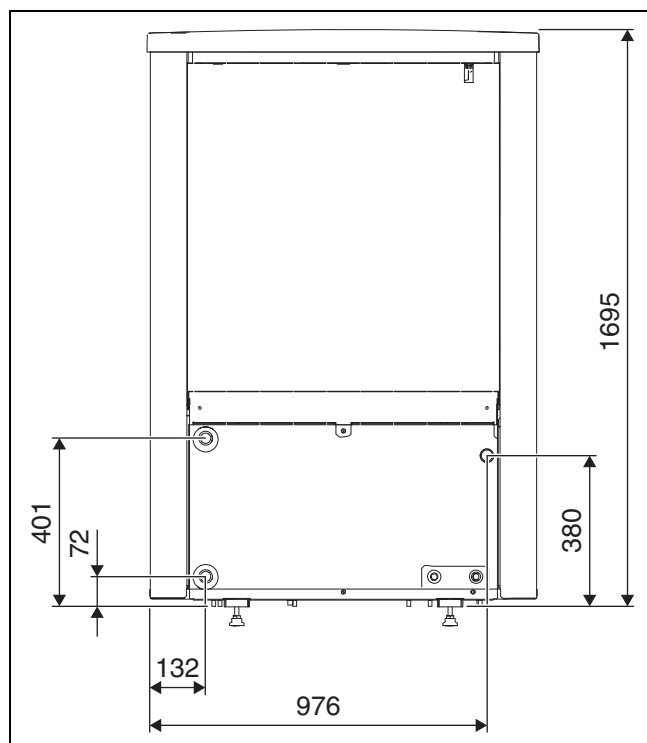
Dimensioni e attacchi del modello di pompa di calore 13-17, lato posteriore
